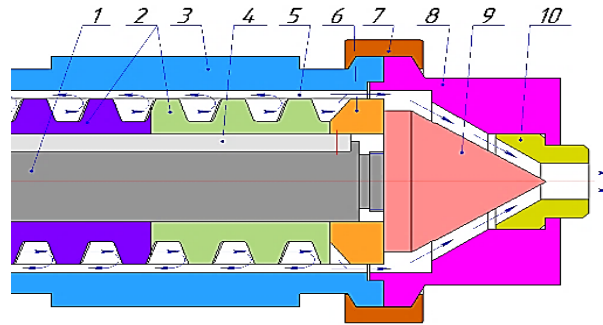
Схема рабочего процесса в выпускающей части шнековой группы: 1 – несущий вал шнека; 2 – шнековые секции; 3 – шнековый корпус; 4 – продольный стопор-шпонка; 5 – корпусные пазы противотока; 6 – затворная втулка; 7 – хомут крепежный; 8 – головка матрицы; 9 – конусный наконечник вала; 10 – матрица фильеры
